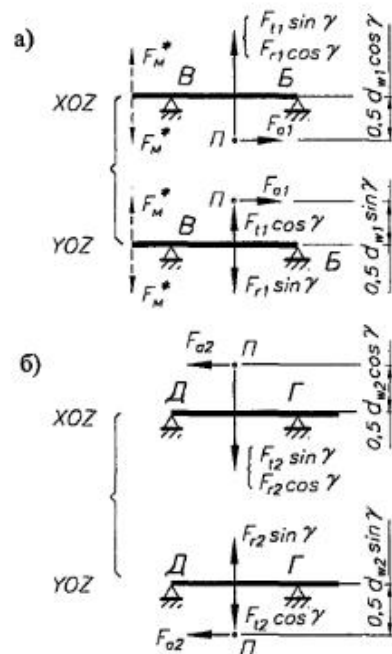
Расчетные схемы: а) вала 1; б) вала 2
